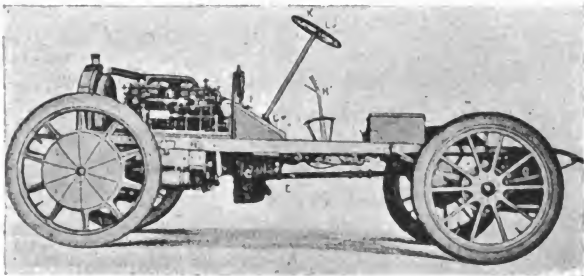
Seitenansicht des Chassis des Lohner-Elektromobils.
